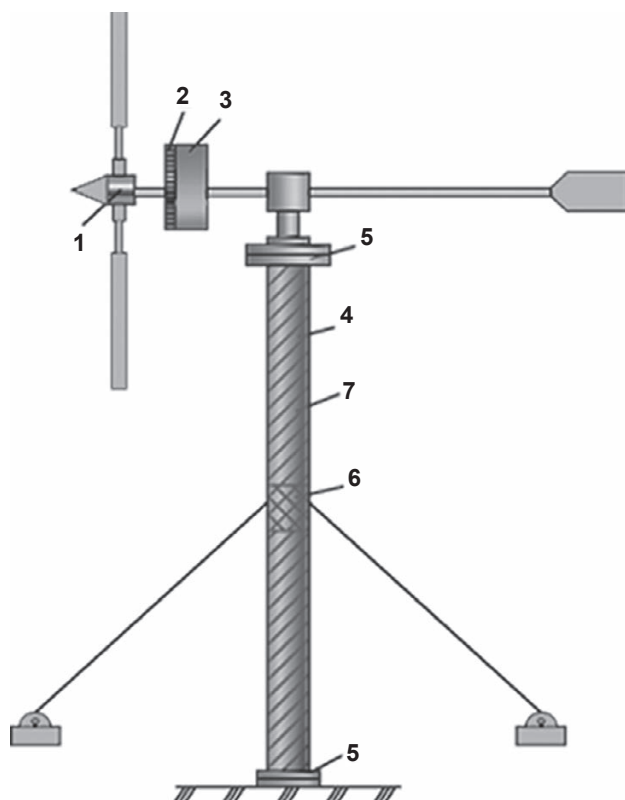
Устройство ветроэнергетической установки: 1 — головка ветроколеса; 2 — редуктор; 3 — электрогенератор; 4 — металлическая труба; 5 — обоймы на концах трубы; 6 — оребренный профиль внутри трубы; 7 — мачта
